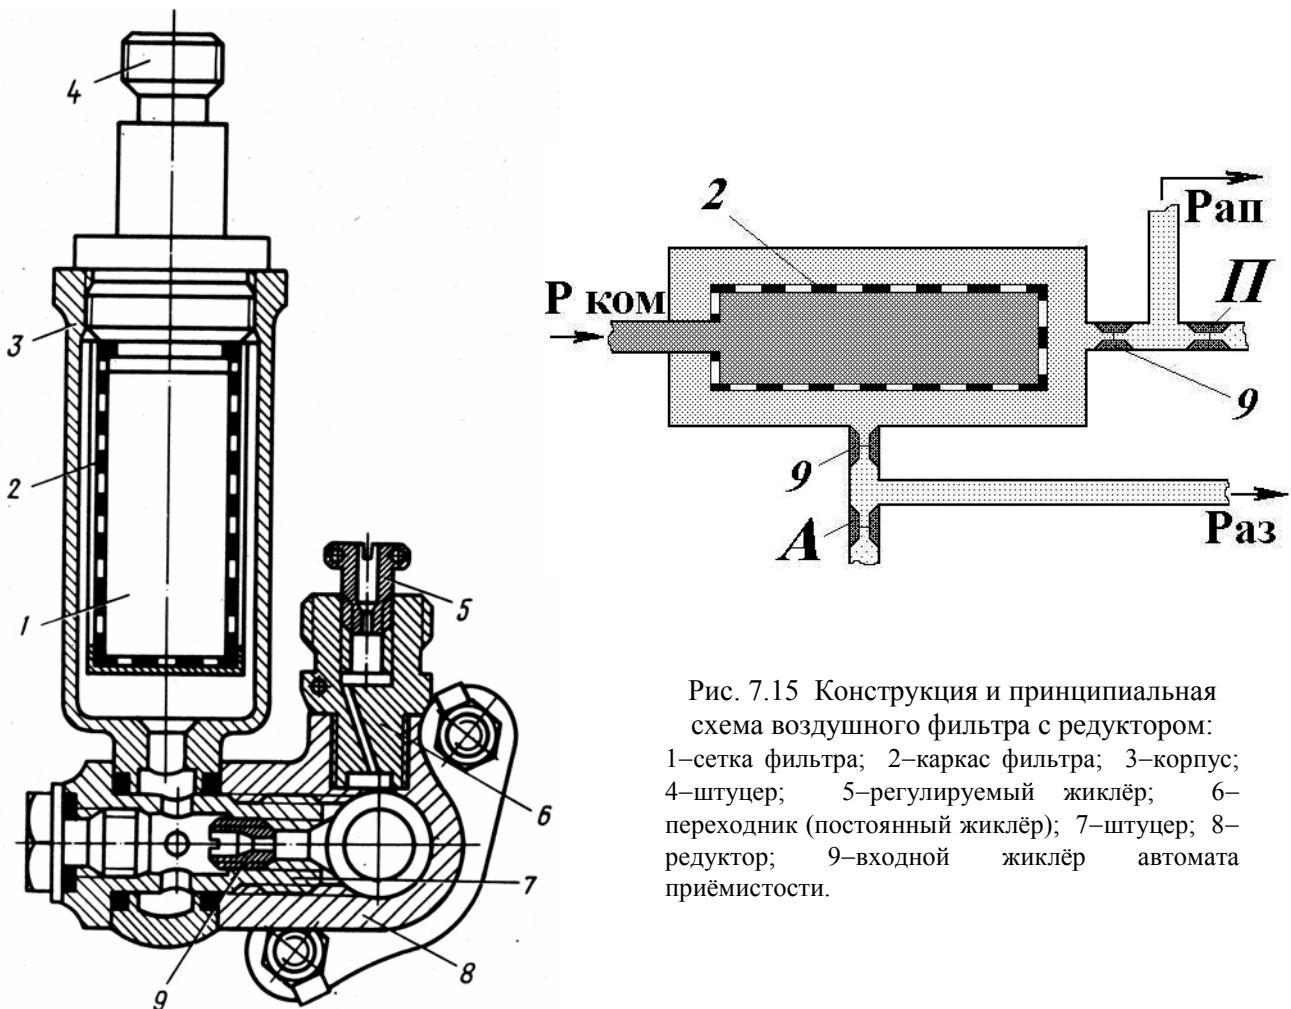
Конструкция и принципиальная схема воздушного фильтра с редуктором:
